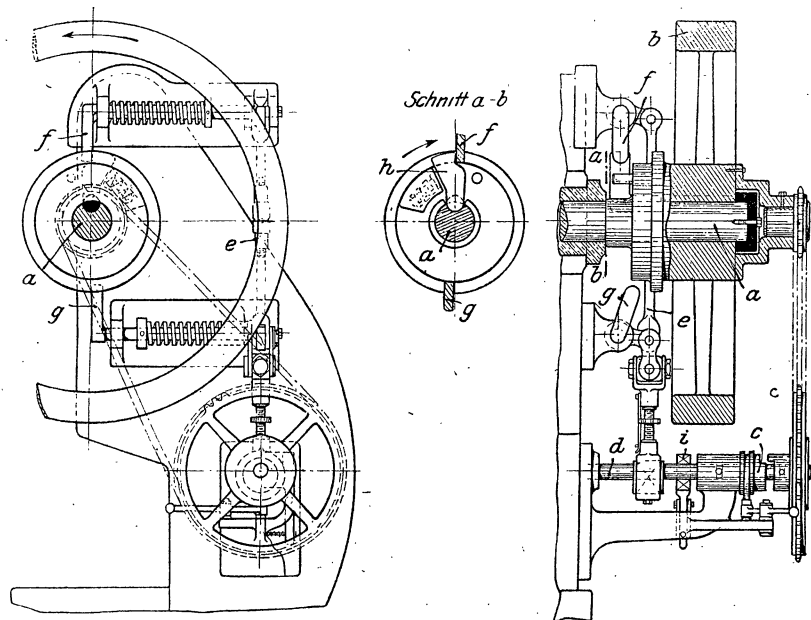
bis 5. Steuerung für Exzenterpressen.
